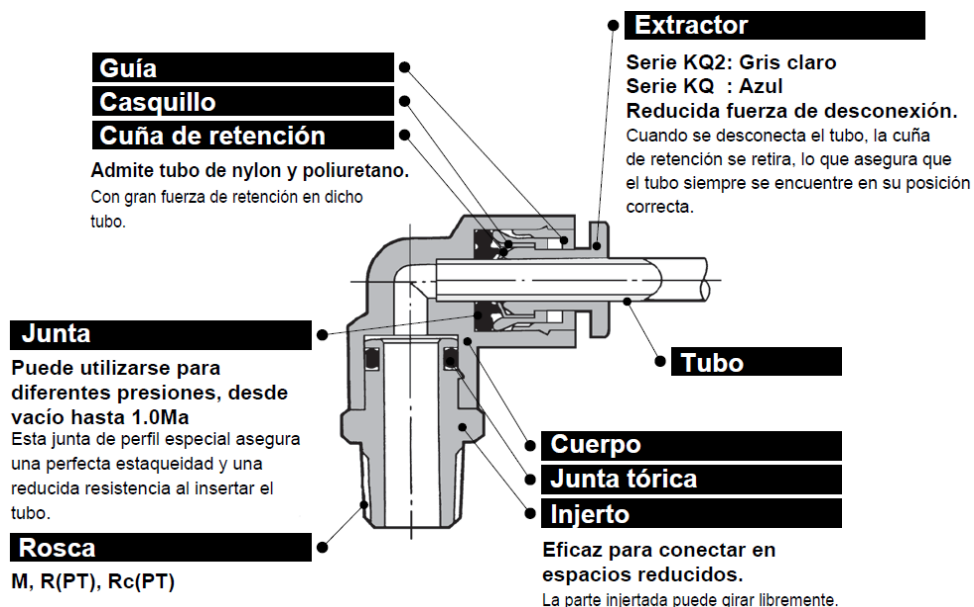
Disposición de las partes de un racor KQ2 (SMC).
